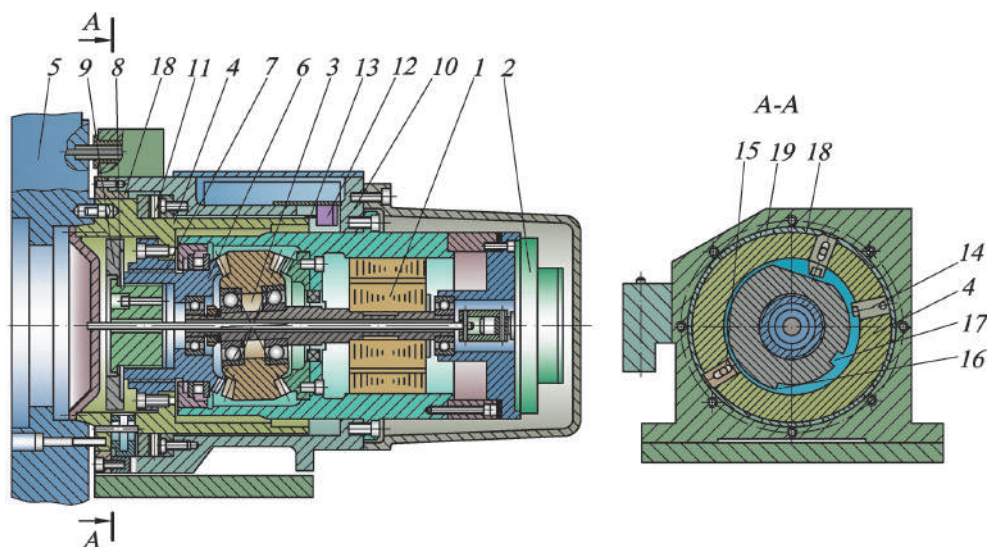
Cap revolver cu transmisie planetară precesională 2K-H [20].
